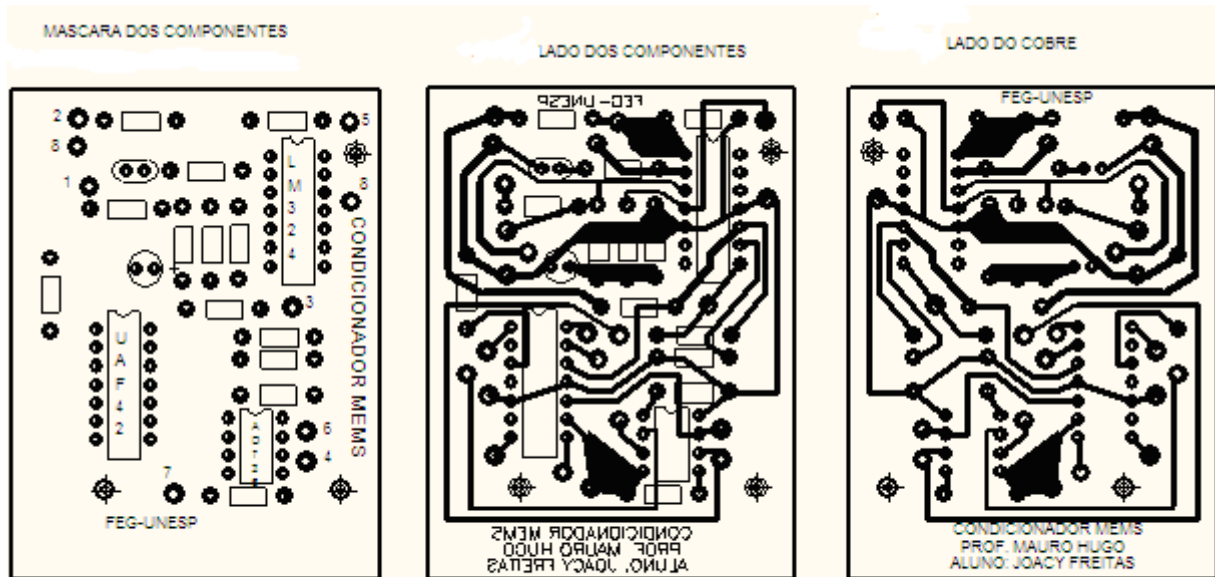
Desenho da placa de circuito impresso – 50mmX65mm.
